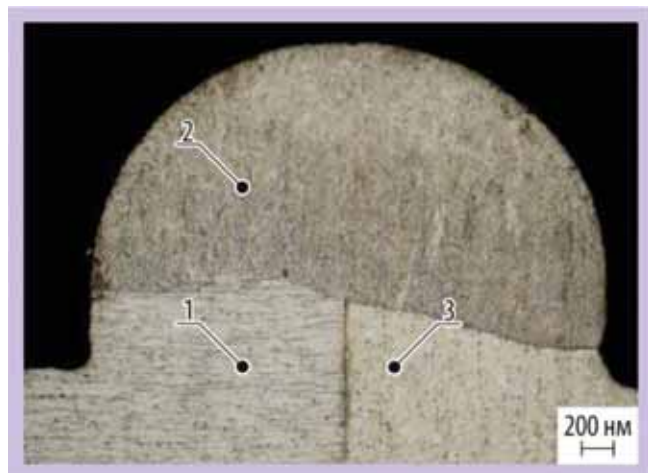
Структура сварного соединения макета источника нейтрино:
